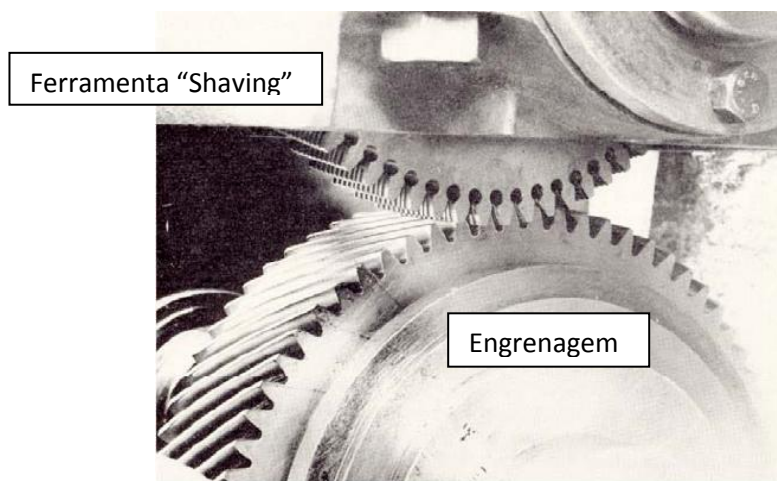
Ferramenta de “shaving” engrenada na engrenagem
